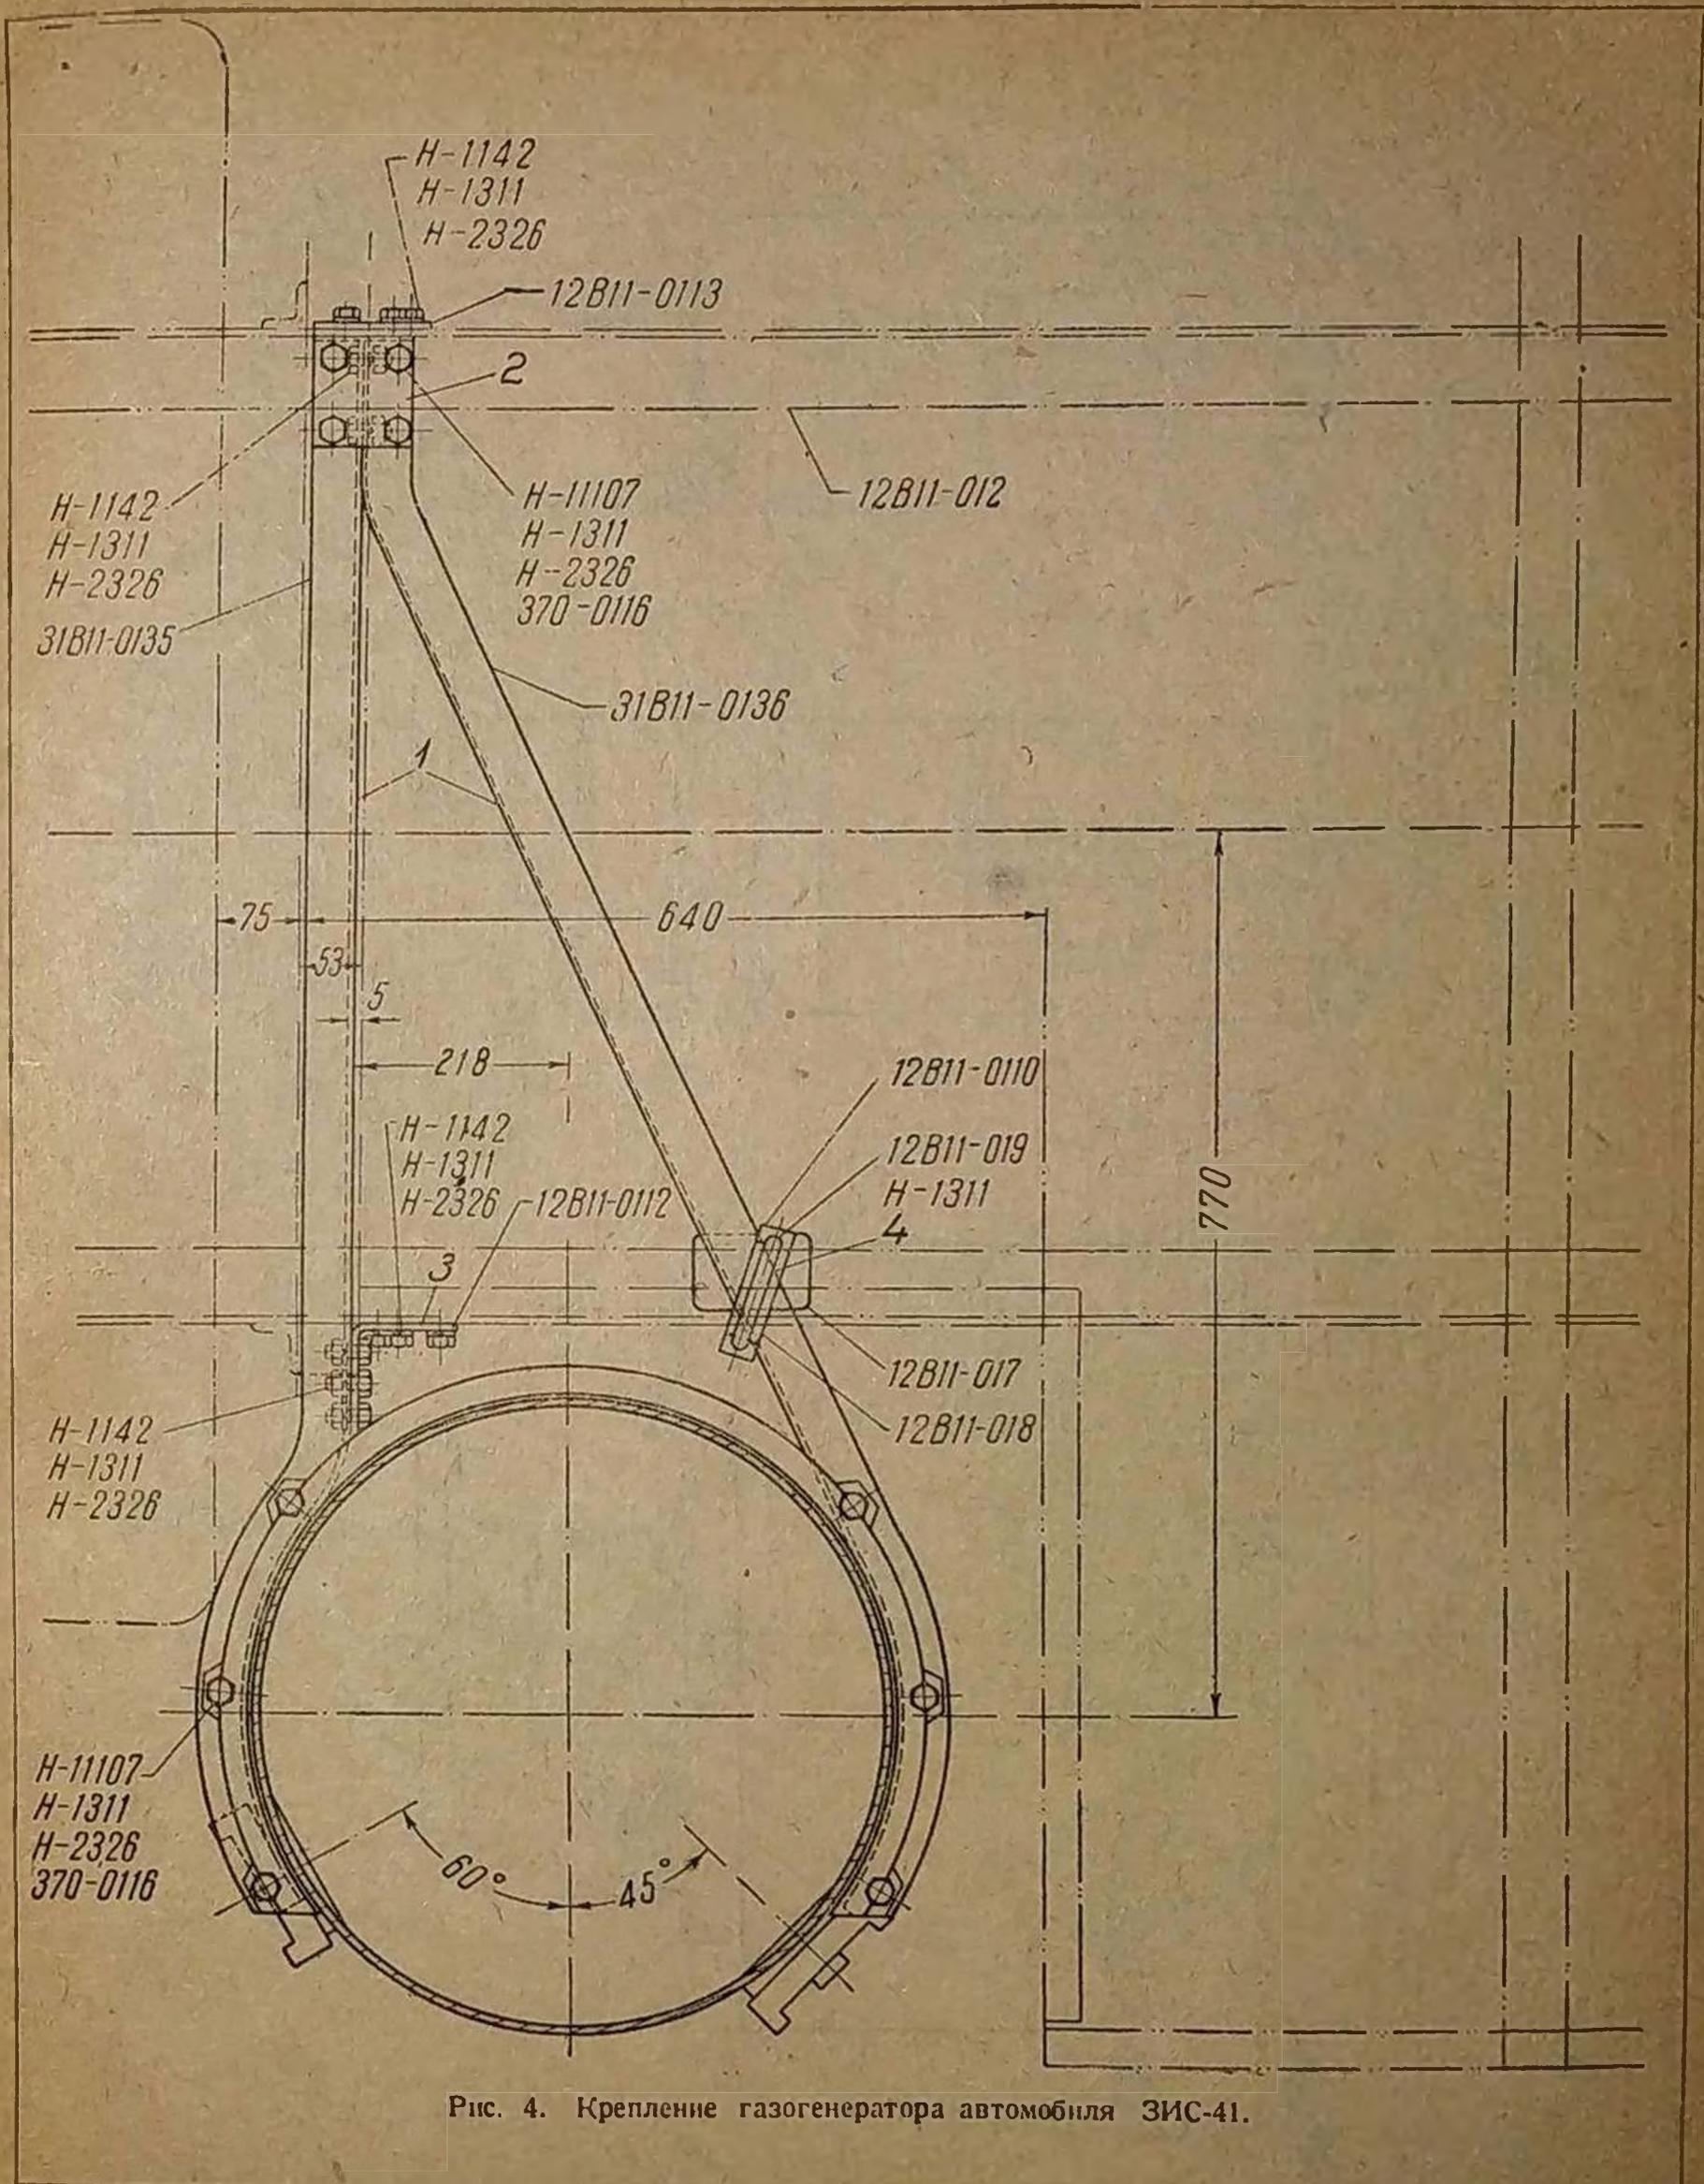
Крепление газогенератора автомобиля ЗИС-41.
